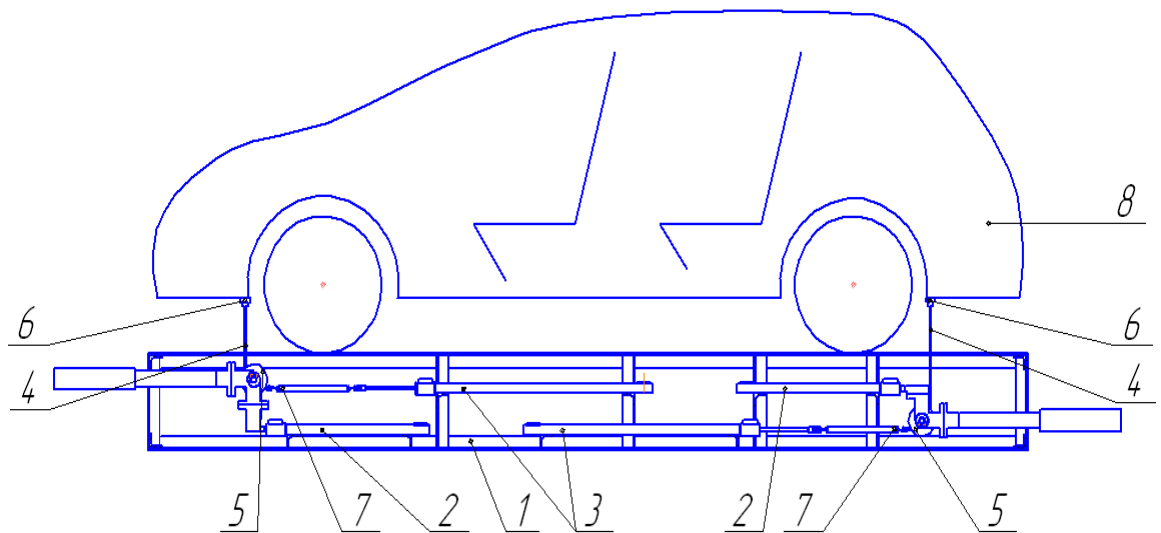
Схема приспособления стенда для нагрузки колес
